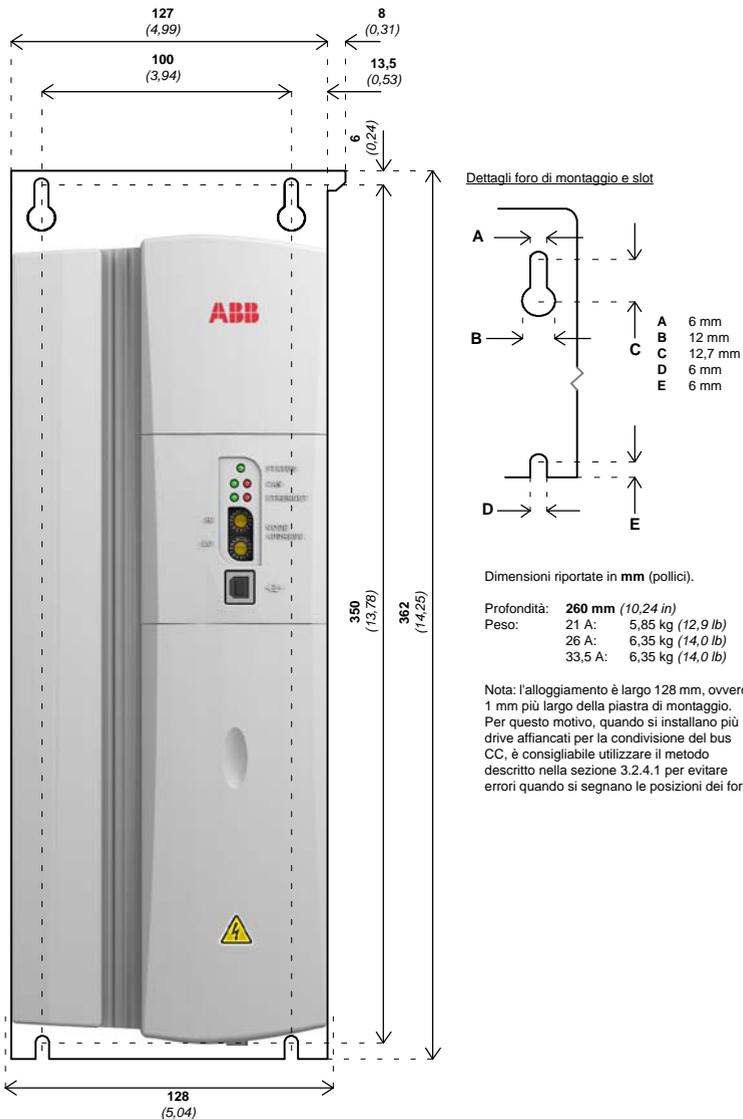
Dimensioni complessive e di montaggio - modelli a 21 A ~ 33,5 A
